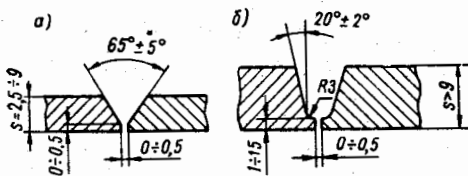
Конструктивные элементы подготовки кромок стыковых соединений труб из стали X18H10T, 0X18H12B и X17H13M2T, свариваемых стык ручной аргонодуговой сваркой (по ОН 26-01-71-68): а — V-образная разделка кромок; б — V-образная разделка кромок с криволинейным скосом
